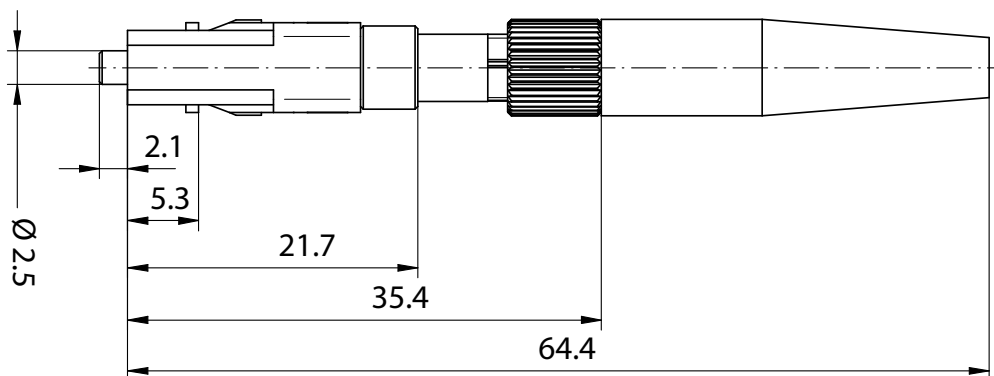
Abmessungen SC-Klemmsteckverbinder, ohne Griffteil
